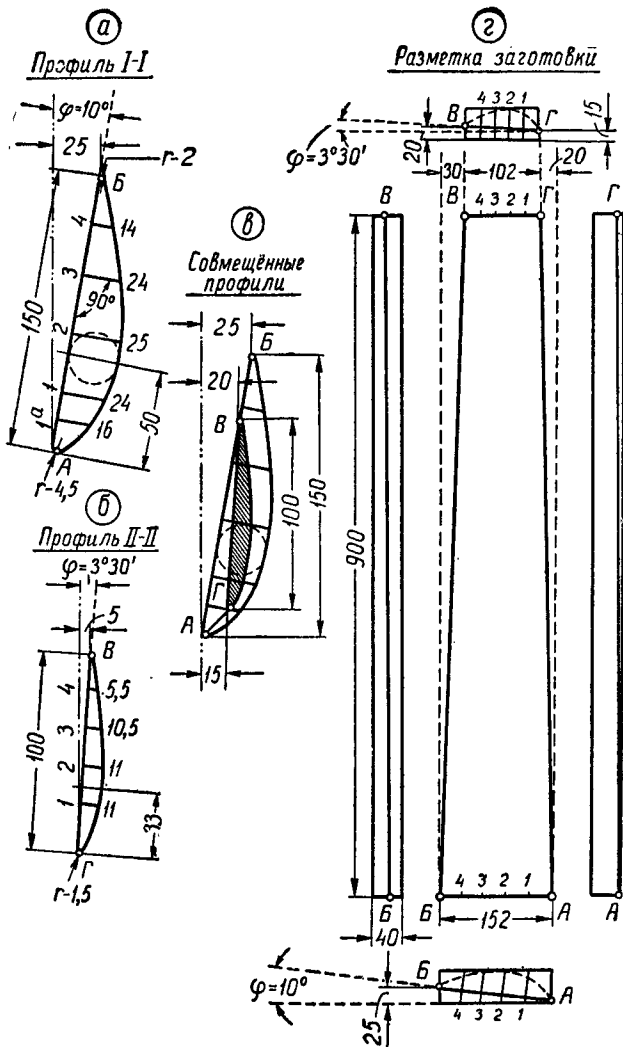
Разметка деревянной лопасти ветроколеса: а — профиль у основания лопасти; б — профиль у конца лопасти; в — совмещенные профили; г — разметка заготовки
